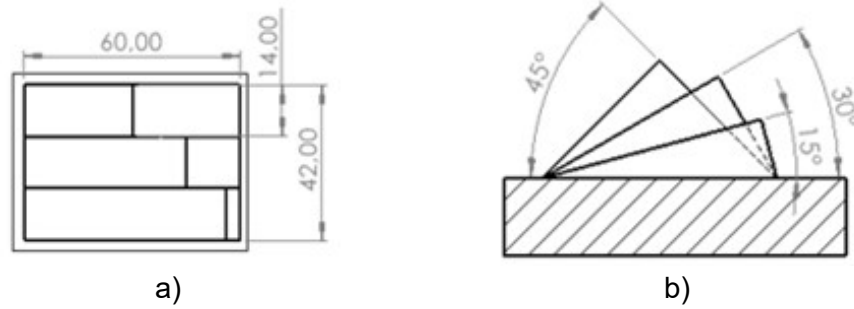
Geometría de las pendientes (a) Planta (b) Perfil.
